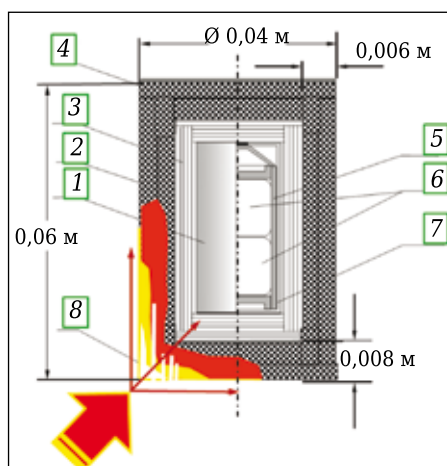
Схема конструкции корпуса РИТ изделия «Ангел»: 1 — металлический корпус; 2 — углерод-углеродный корпус; 3 — углеродная теплозащита; 4 — углерод-углеродная композитная крышка; 5 — конструкция металлического корпуса; 6 — таблетки радиоизотопного материала; 7 — графитовый корпус; 8 — схема этапа прогрева
